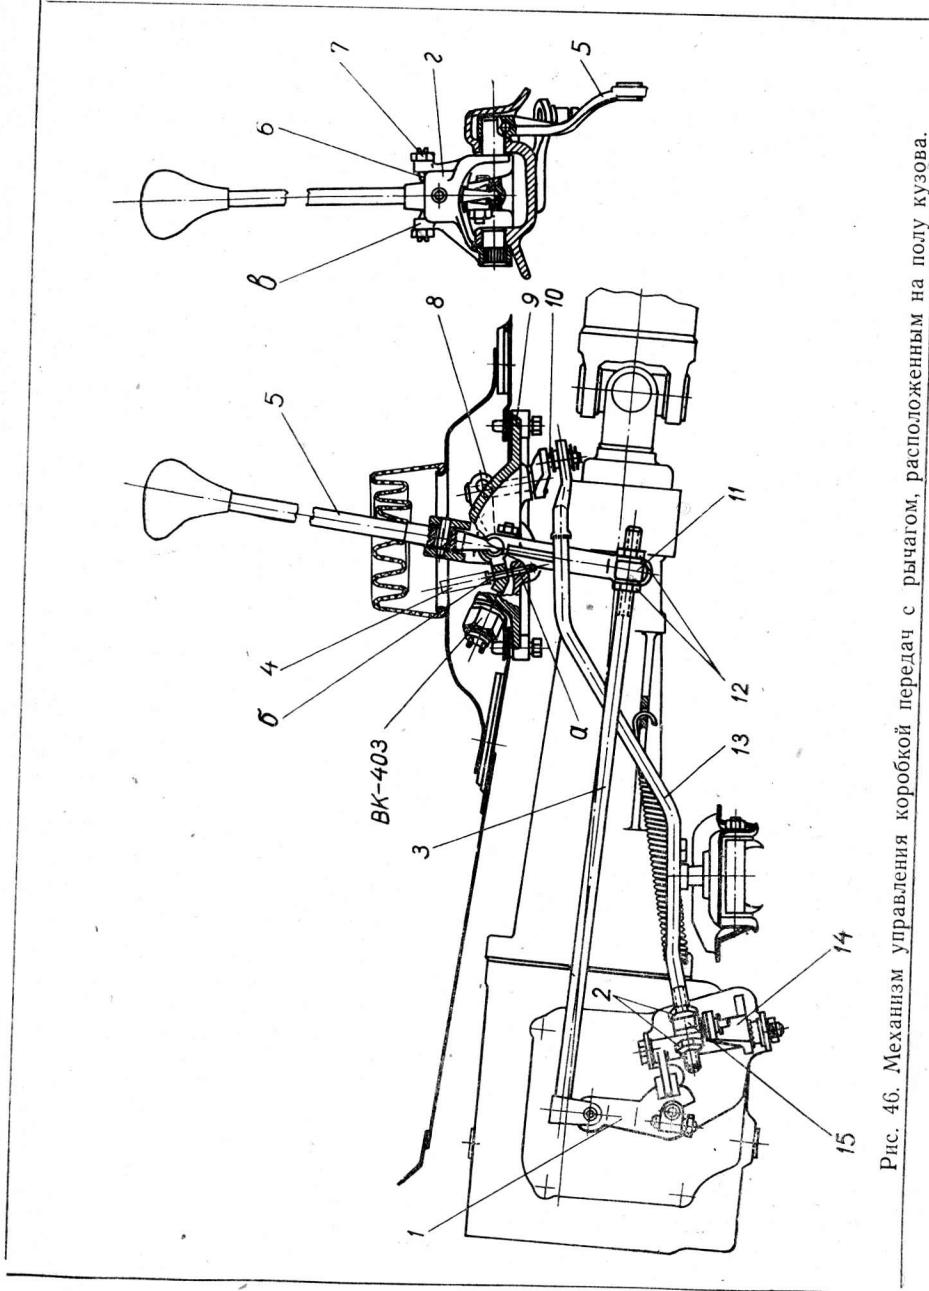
Механизм управления коробкой передач с рычагом, расположенным на полу кузова.
